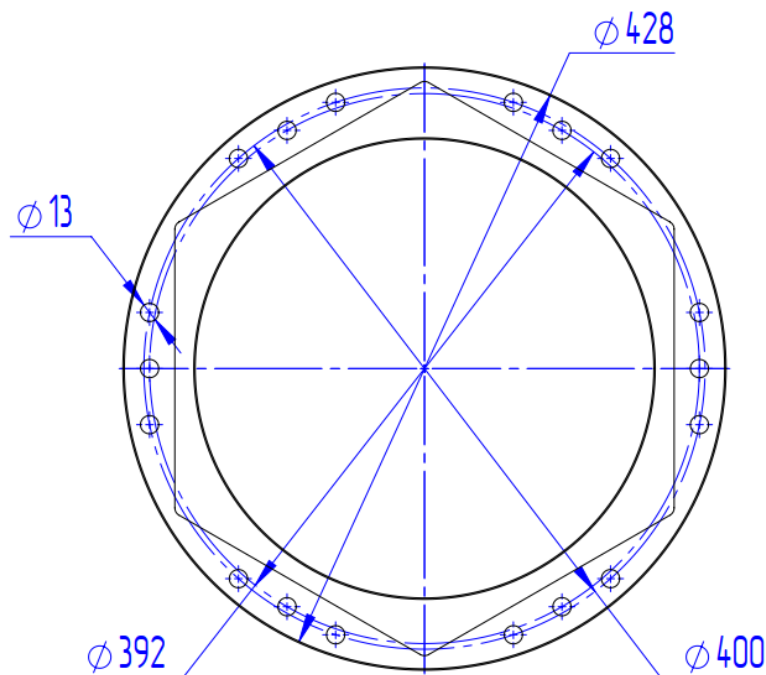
Габаритные размеры переходного фланца ОПУ.
